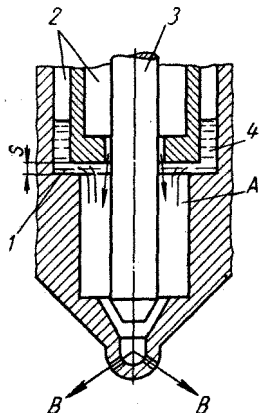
Схема типичной форсунки для компрессорного распыла:
